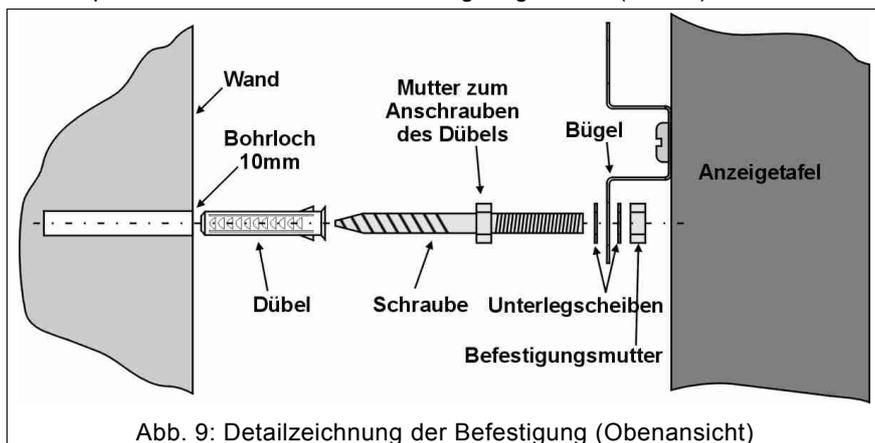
Detailzeichnung der Befestigung (Obenansicht)
